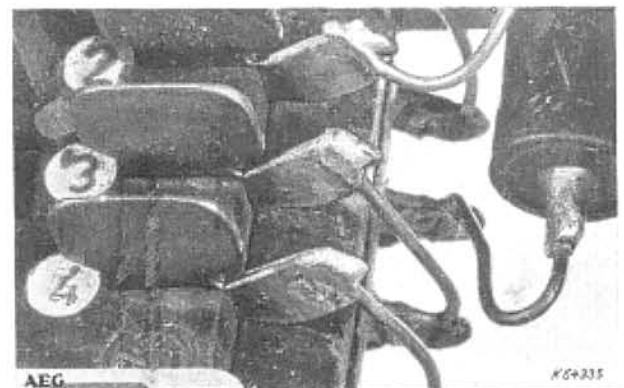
Gut ausgeführte Schweißung von Kupferdraht an Bronze-Messerkontakten.
